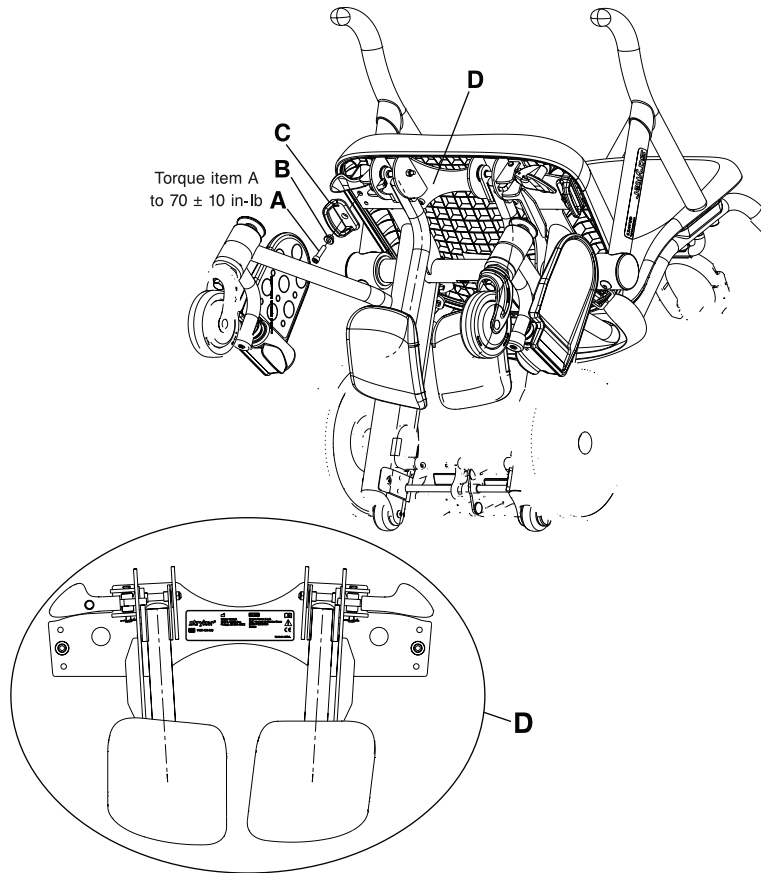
Assemblage soudé du repose-jambes
